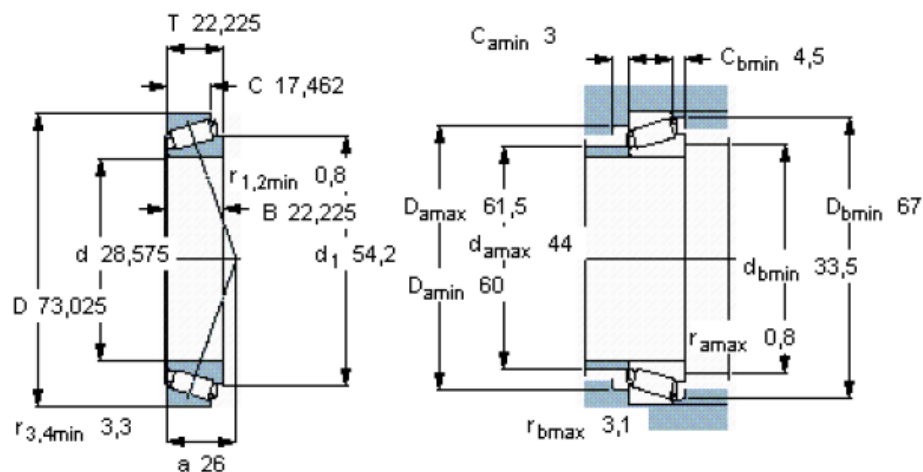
Dimensiones del cojinete 02872/02820/Q [14].
